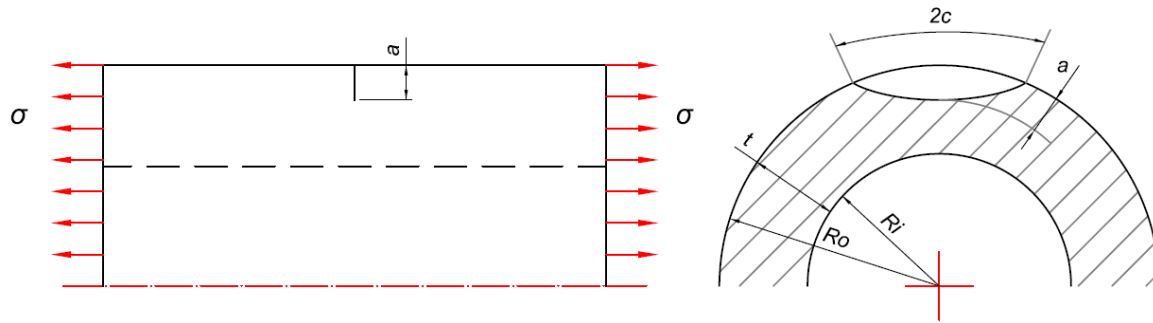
Tubería con fisura semi-elíptica externa en dirección transversal sometida a carga axial.
